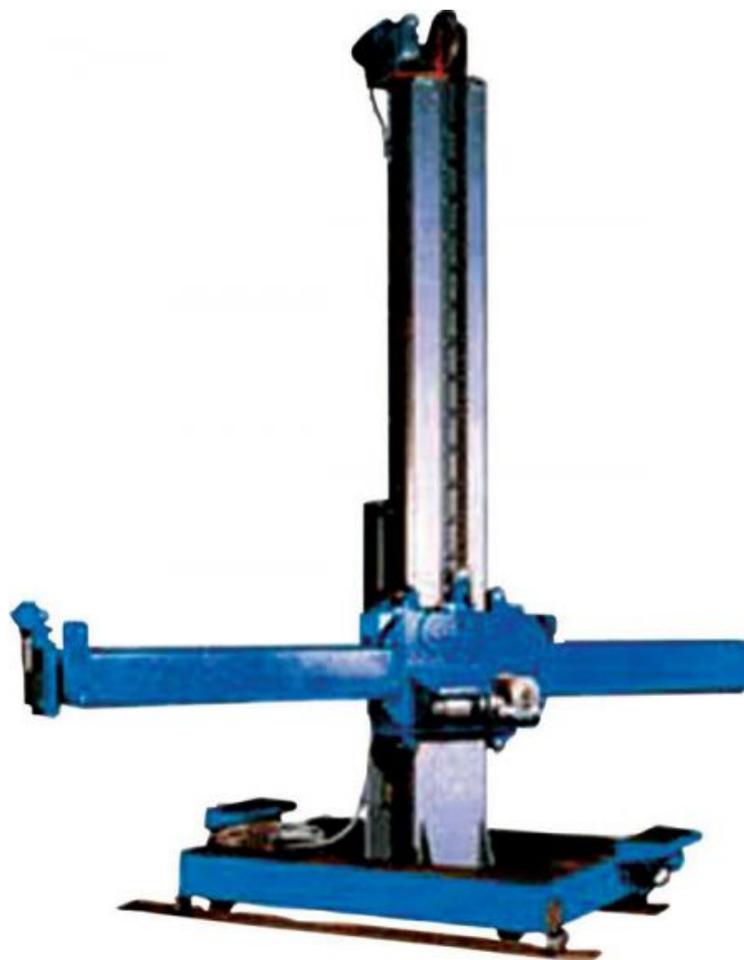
Общий вид сварочной колонны BCZQ 2x2
